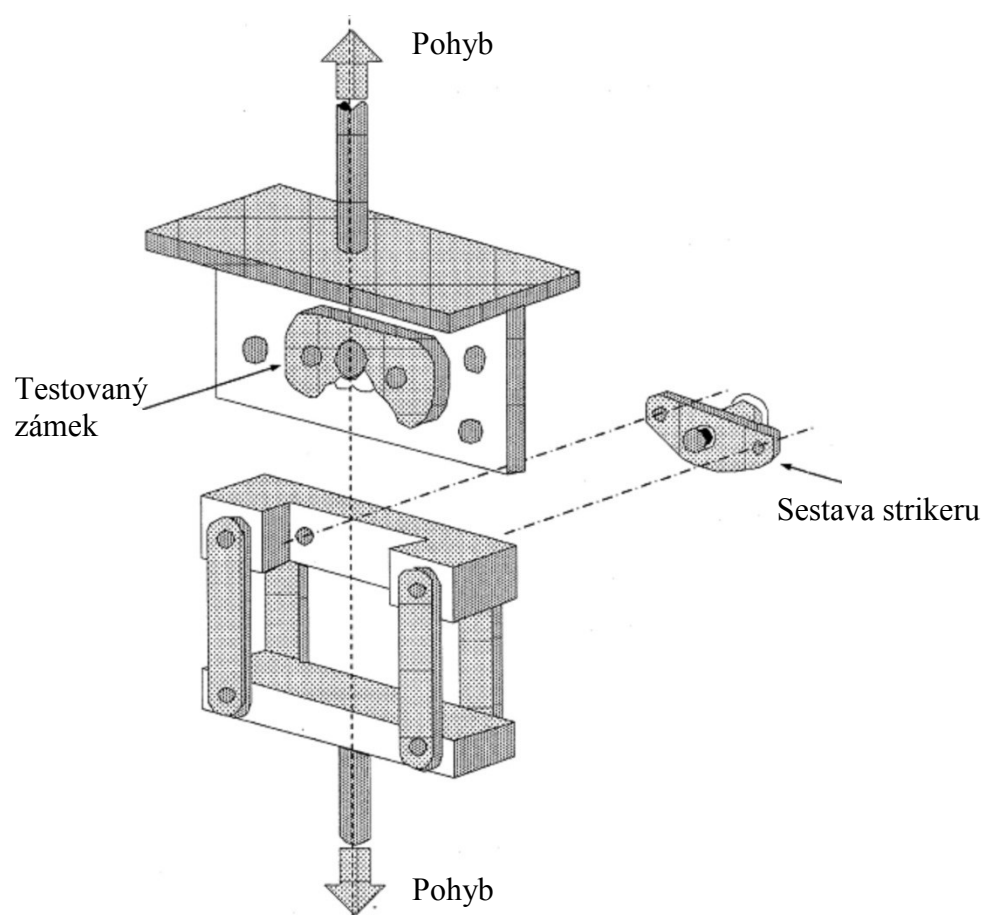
Zobrazení zátěžového testu 1 [6]
